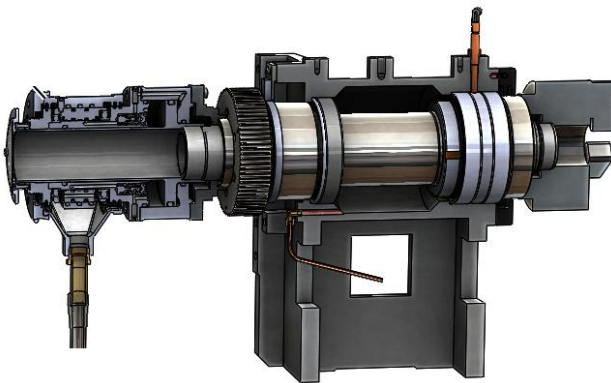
Корпус шпиндельной бабки станка с ЧПУ HAAS ST-25 (США)
